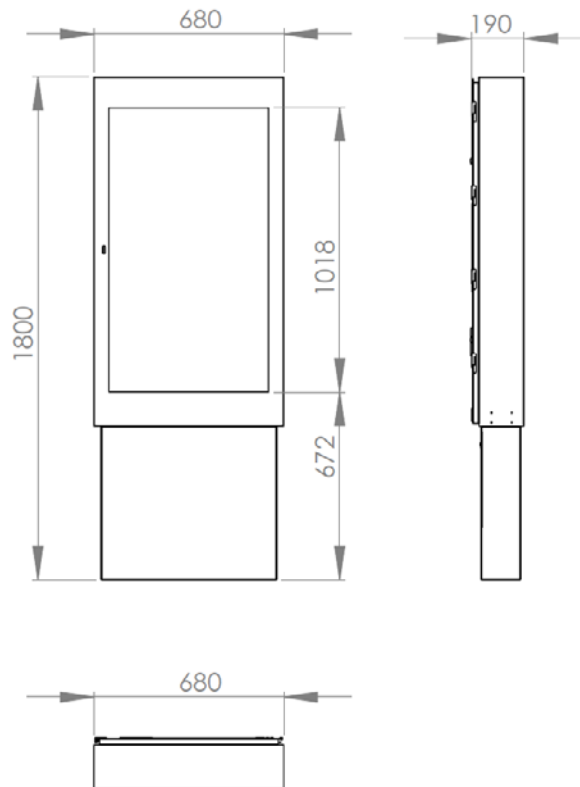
DIB 600 PREMIUM, Dimensions en mm
